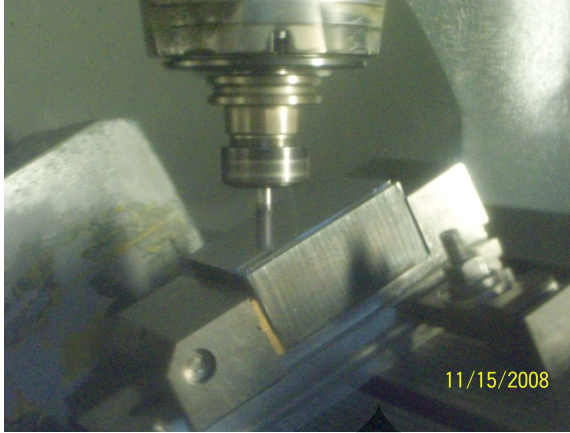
Mesin Milling 5Aksis DMU 50e
